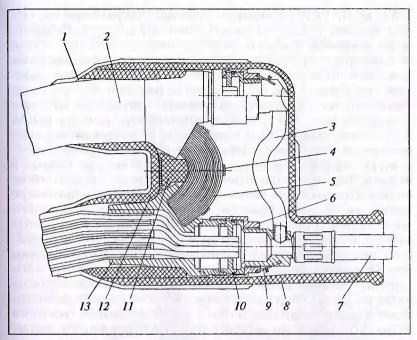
Головка обмотки статора турбогенератора ТГВ-200М-2: I — заполнитель-замазка; 2 — стержень; 3 — соединительный патрубок; 4 — шнуровой бандаж; 5 — медные пластины; 6 — специальная гайка; 7 — фторопластовый шланг; 8, 12 — колпачки; 9 — проволока; 10 — уплотняющие прокладки; 11 — колодки; 13 — наконечник
